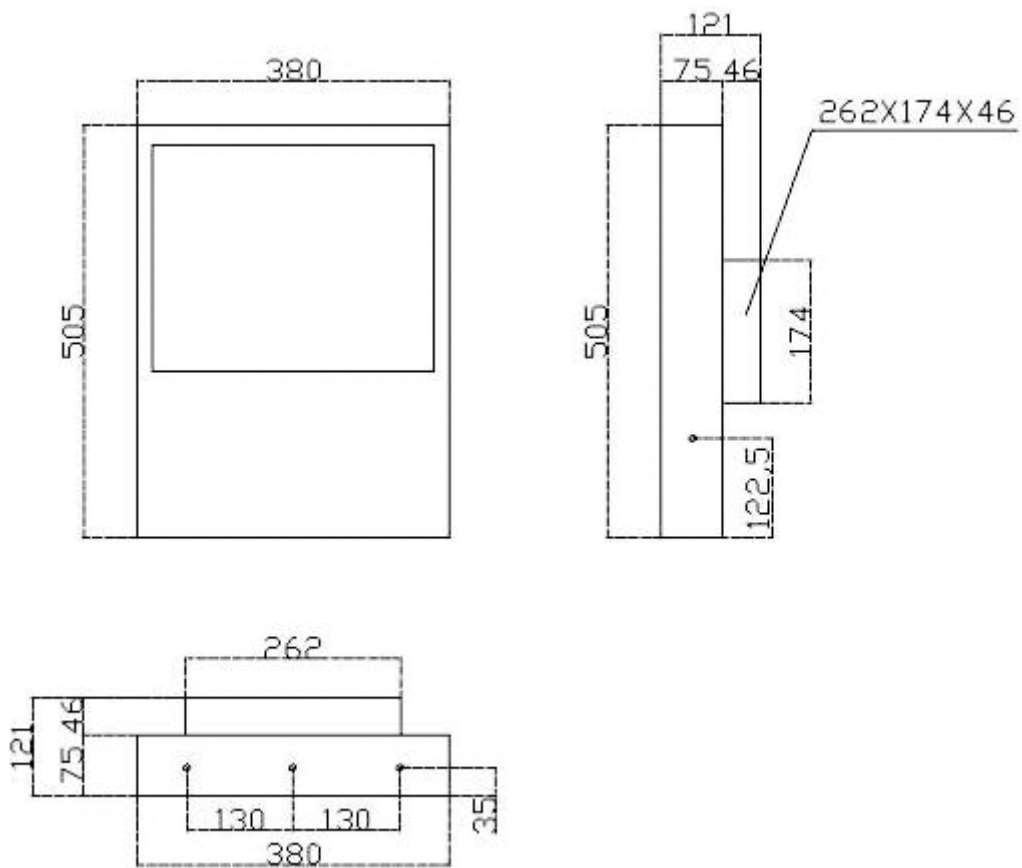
Установочные размеры ЧПУ контроллера FX450B.
